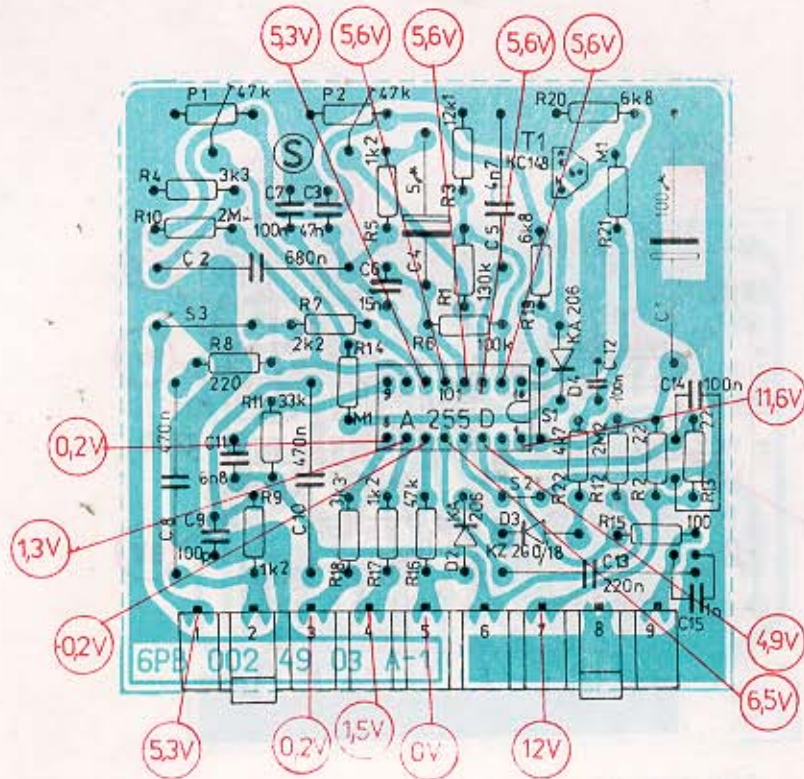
MODUL "Z" 6PN 053 74 - POHLAD ZO STRANY SPOJOV
